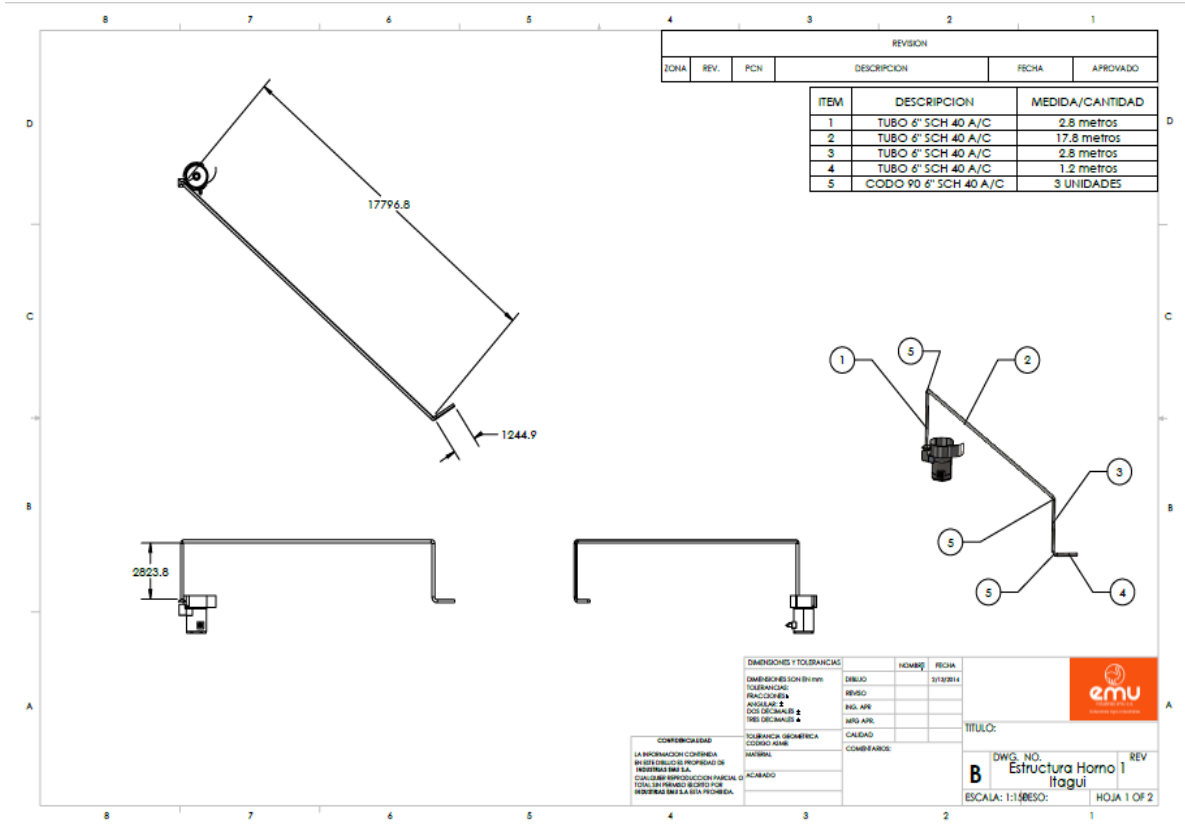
Plano detallado de la tubería para la conducción de calor entre los hornos (Esquema suministrado por industrias EMU. S.A.)
